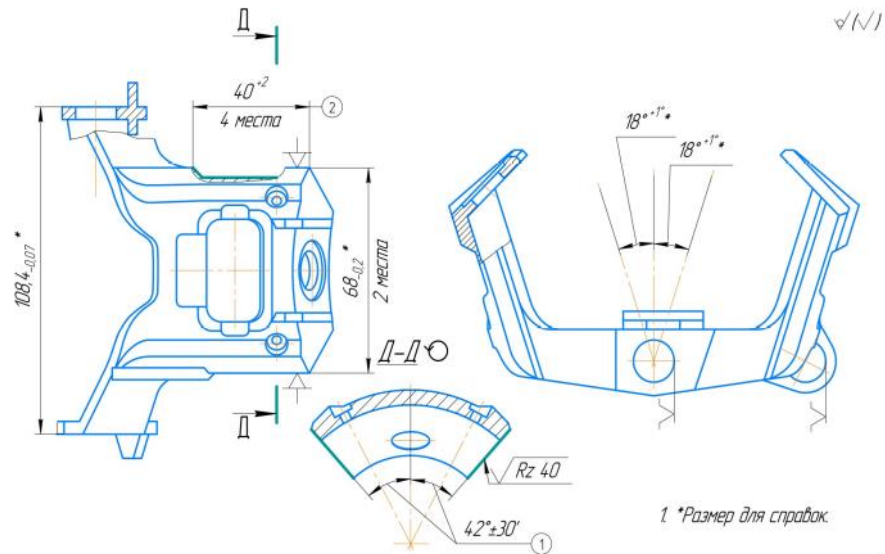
Эскиз к операции 120 – Фрезерная с ЧПУ
